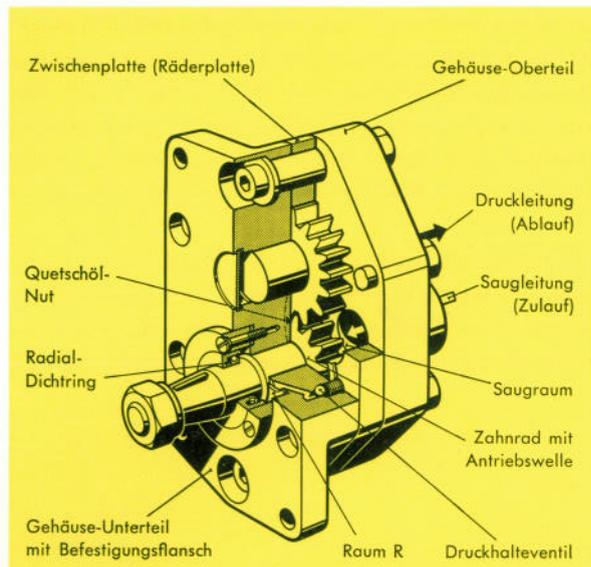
Bosch-Plattenpumpe HY/ZE ..
